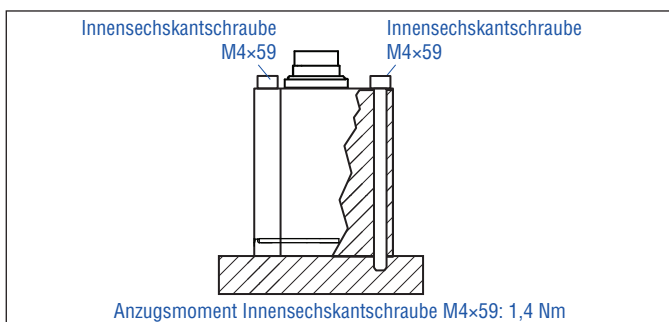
Befestigung mittels Innensechskantschrauben M4×59
